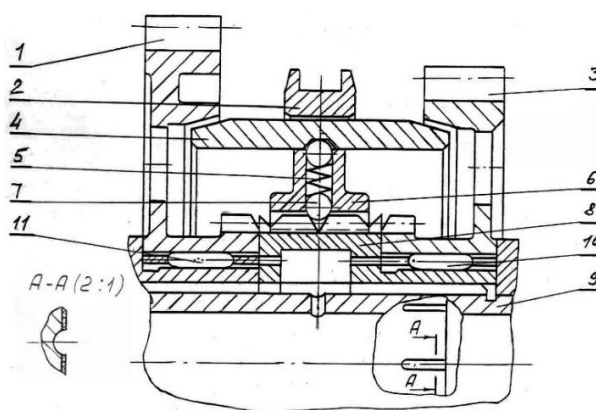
Инерционный конусный синхронизатор коробки передач:
